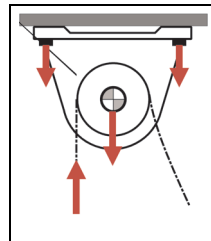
Ungünstige Beanspruchung von Graugussgehäuse und Befestigungsschrauben
